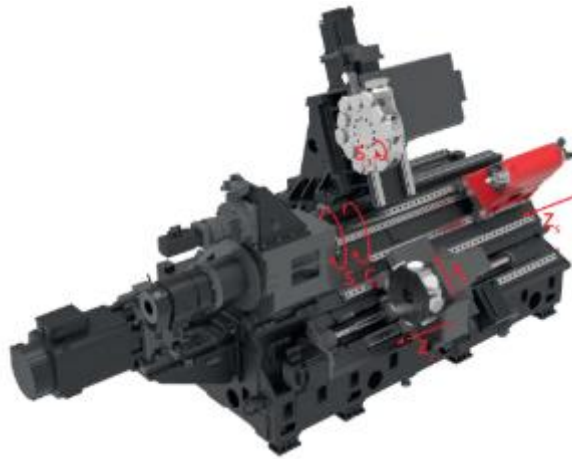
Pracovní prostor stroje SP 430 MC [25]
